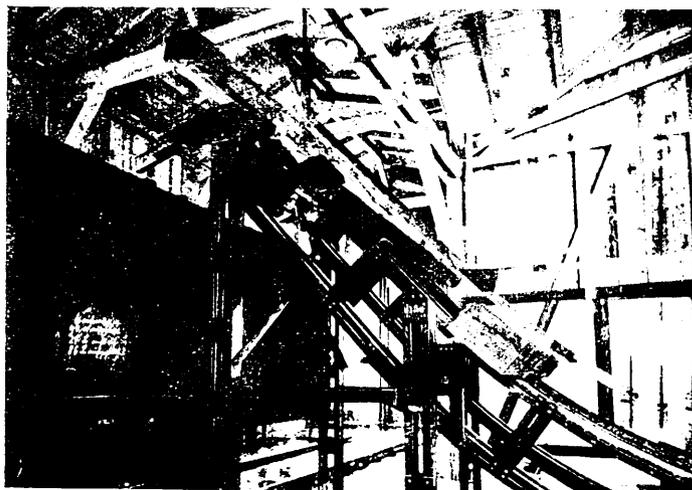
Verladevorrichtung für die aufgeplatteten Schwellen.
